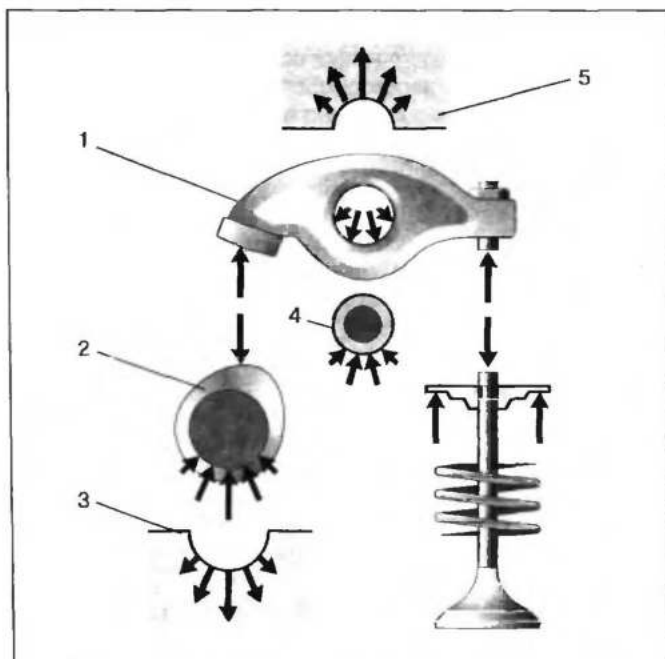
Усилия на детали в схеме привода клапана коромыслом: 1 — коромысло; 2 — распределительный вал; 3 — опора распределительного вала; 4 — ось коромысел; 5 — опора оси
